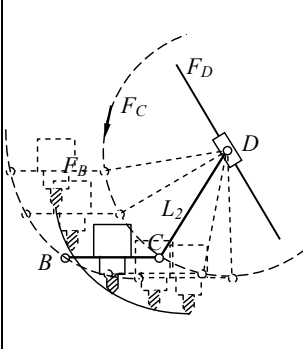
Багатокоординатний свердлильно-фрезерний верстат підвищеної жорсткості:
